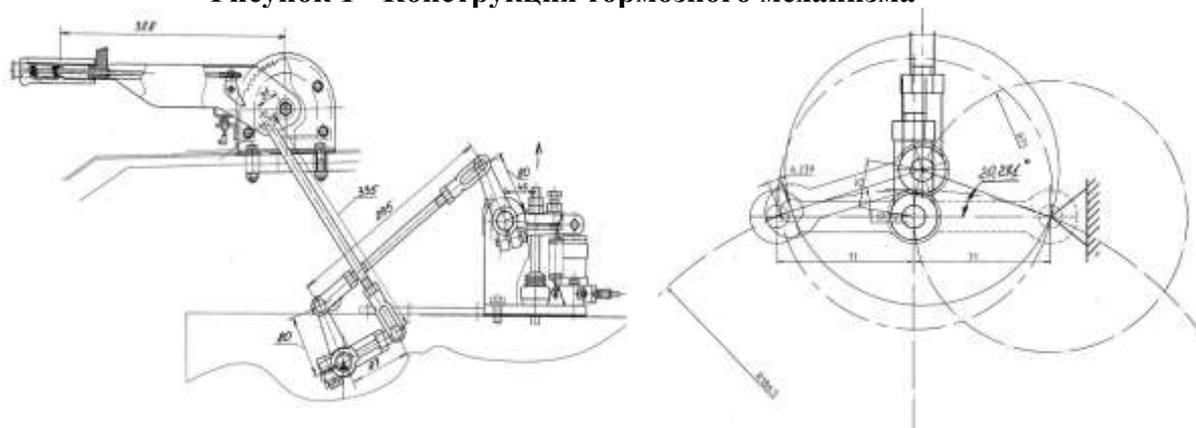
Конструкция привода стояночно-запасного тормоза
